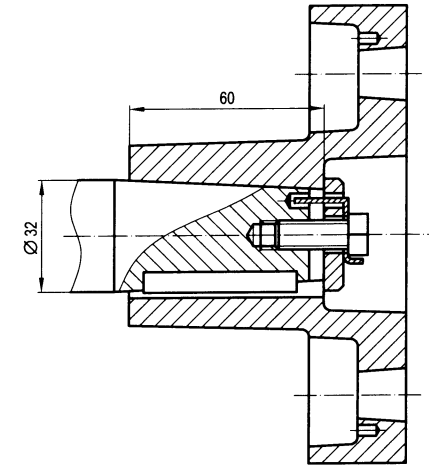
Крепление полушестерни на коническом конце вала
